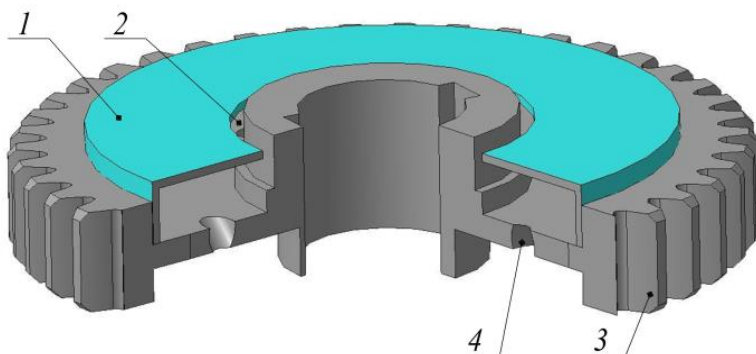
Предлагаемая конструкция шестерни, в полости которой закреплена цилиндрическая вставка
